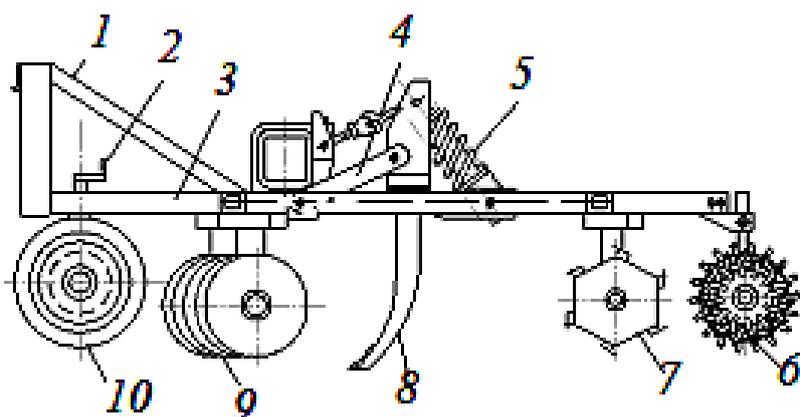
Комбінований агрегат для протиерозійного обробітку ґрунту: 1 - навіска; 2 – регулювальний гвинт; 3 – несуча система; 4 – паралелограмний механізм; 5 – пружина; 6 – барабан-вирівнювач; 7 – штангово-зубчастий коток; 8 – плоскоріжучі вузькозахватні лапи; 9 – дискові батареї; 10 – опорні колеса
